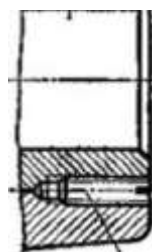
Подшипники скольжения в конструкциях как одно целое со станиной
